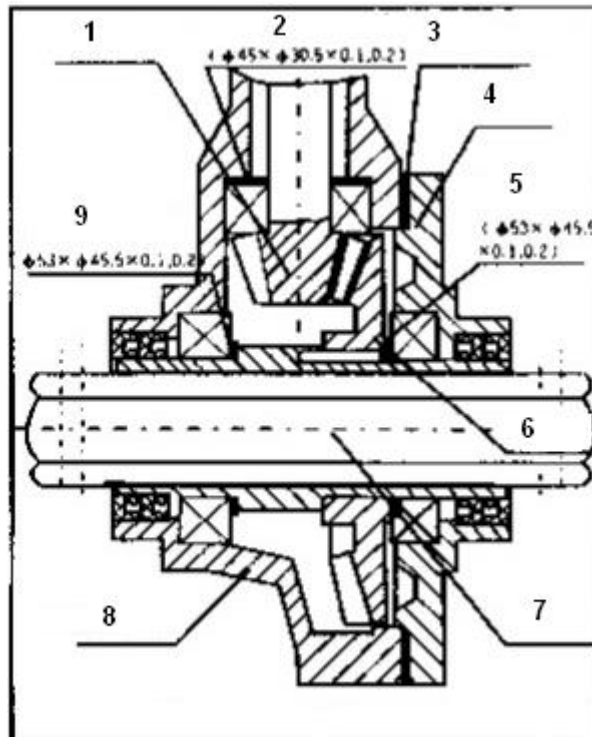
Структурная схема конической зубчатой передачи в ходовой части
